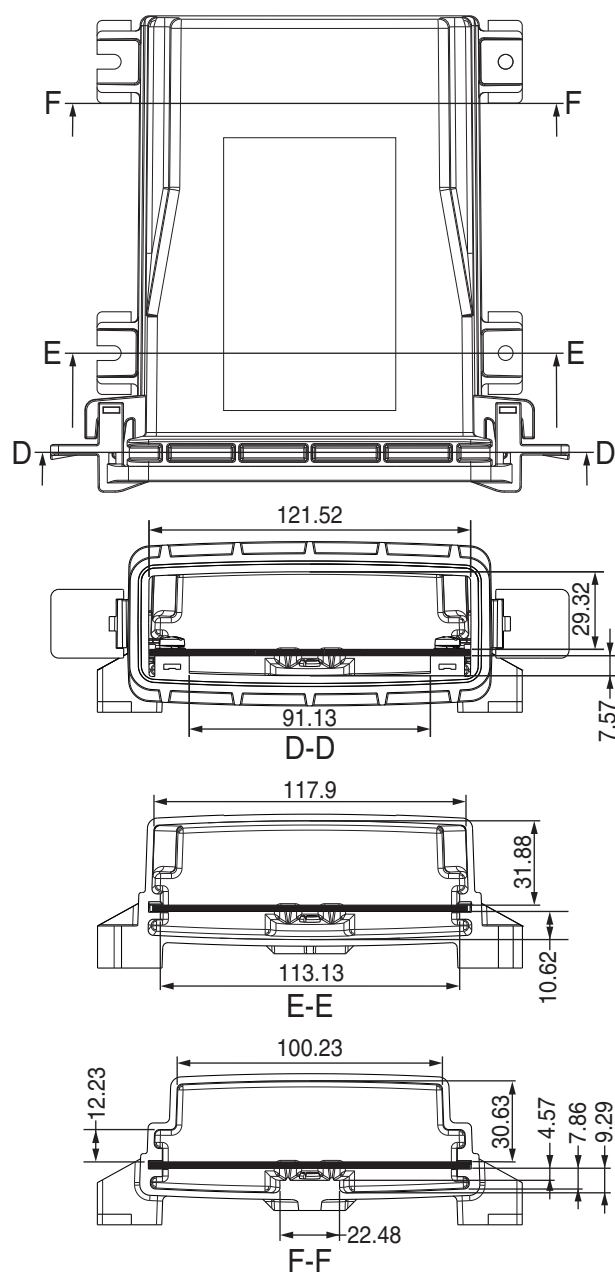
Innenansicht Gehäuse mit Leiterplatte
